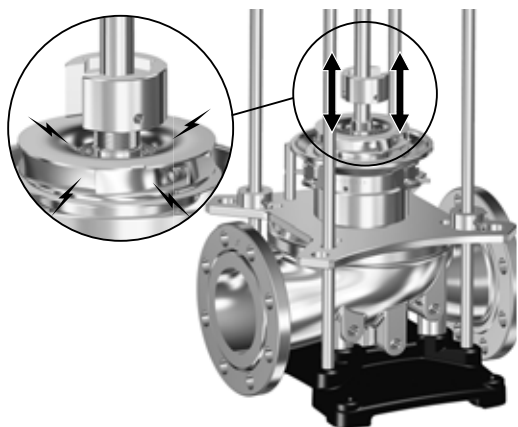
Установка рабочего колеса (49 или 49а) на валу насоса (51) при помощи приспособления С
